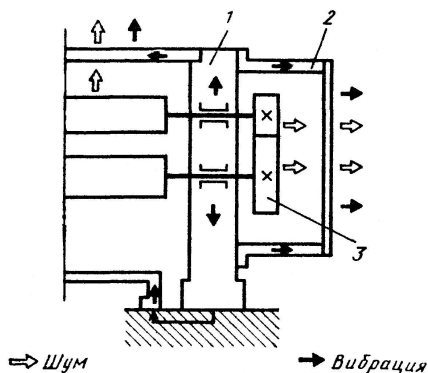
Пути передачи звука и вибрации на ограждения редукторных систем:
